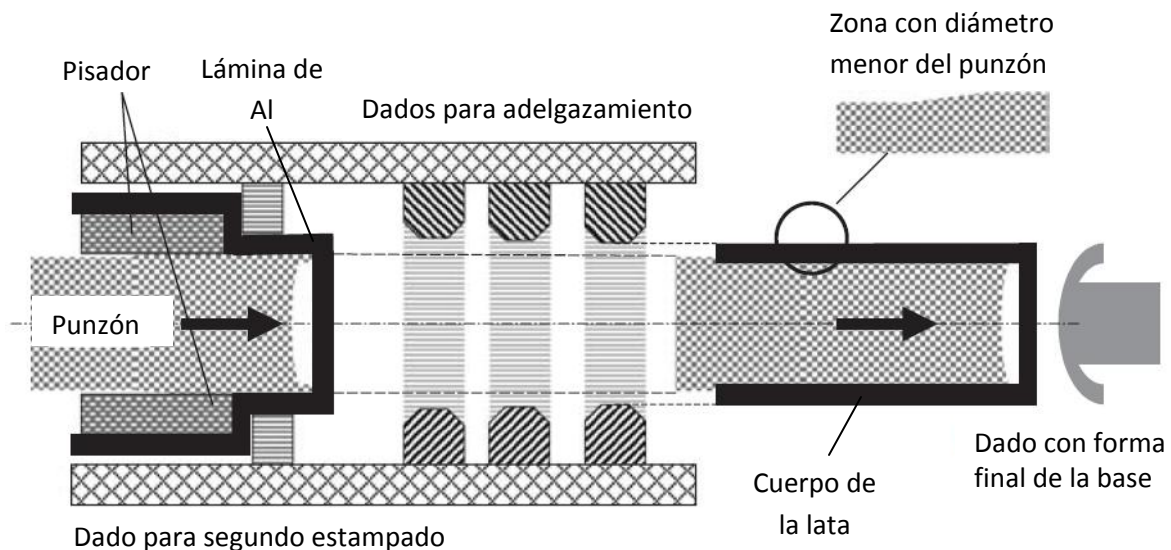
Segundo estampado profundo en la producción de latas de aluminio [2].
